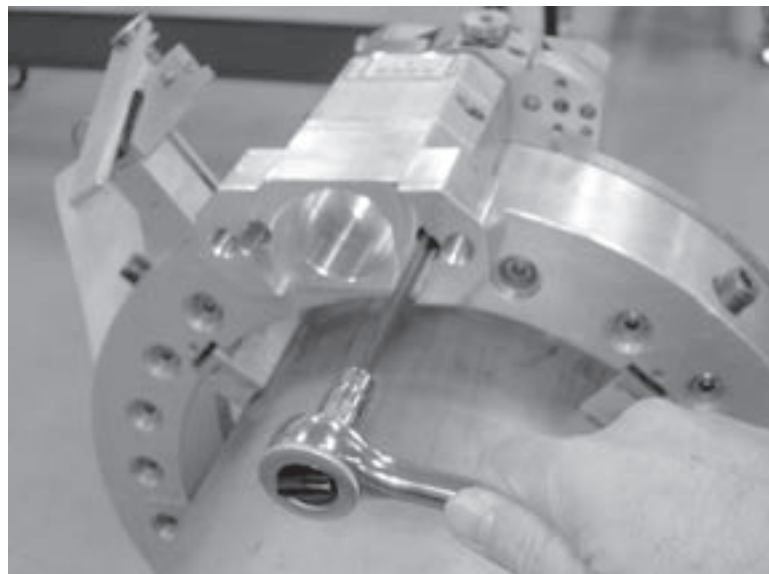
Apriete los 2 tornillos que sostienen el adaptador de la unidad de accionamiento hidráulico a la caja del piñón.
